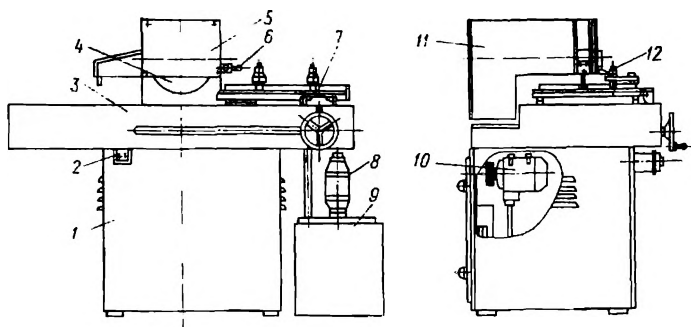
Принципиальная схема окантовочного станка модели CMP-012A
